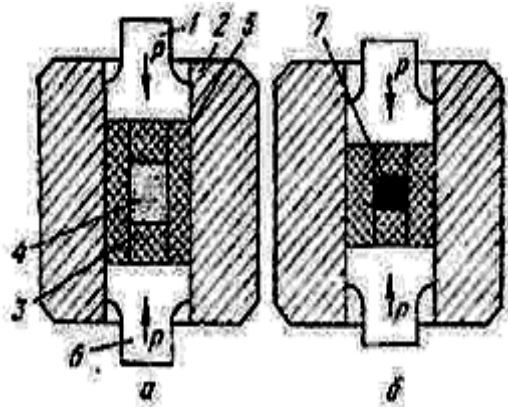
Схема двустороннего прессования в эластичной оболочке: а – в момент приложения давления, б – после прессования; 1-верхний пуансон, 2-матрица пресс-формы, 3-резиновая пробка, 4-порошок, 5-эластичная оболочка, 6-нижний пуансон, 7-заготовка из порошка.
